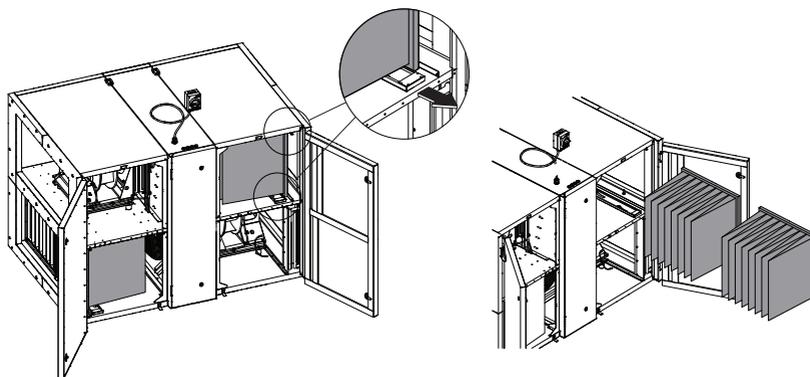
Un exemple montrant comment remplacer les filtres à poches
